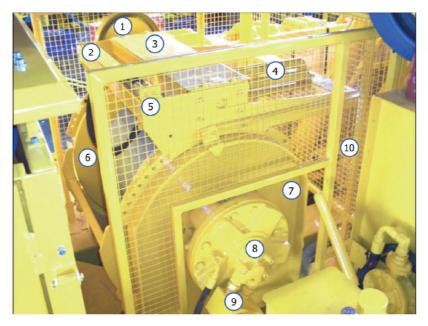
Вспомогательная лебедка поддона: 1 – привод и цепь намоточного механизма; 2 – рама намоточного механизма; 3 – намоточный механизм под кожухом; 4 – направляющий ролик под кожухом; 5 – ниппели для смазки; 6 – барабан лебедки; 7 – боковая пластина приводного двигателя вспомогательной лебедки; 8 – приводной двигатель вспомогательной лебедки; 9 – двойной уравновешивающий клапан в сборе; 10 – часть кожуха вокруг вспомогательной лебедки
